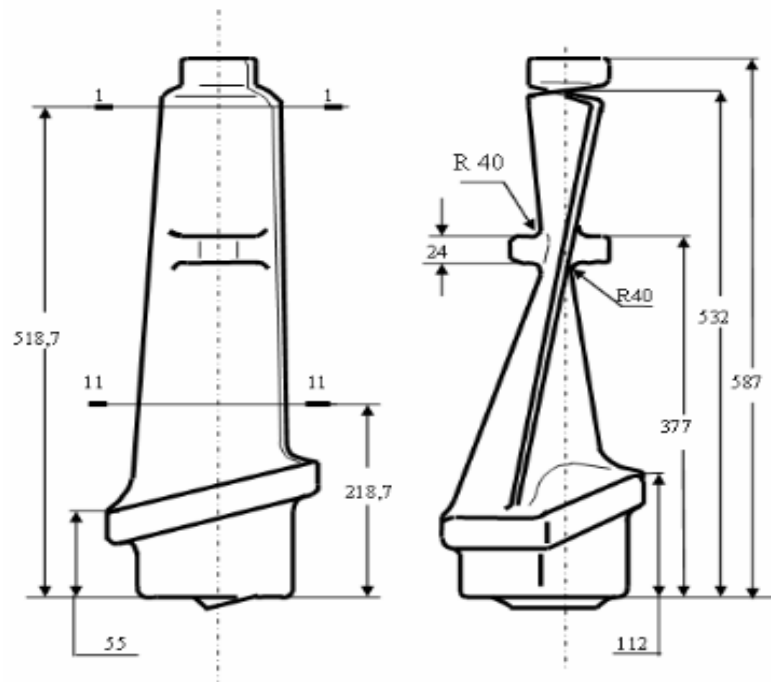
Вихідна заготовка лопатки першої ступені компресора
